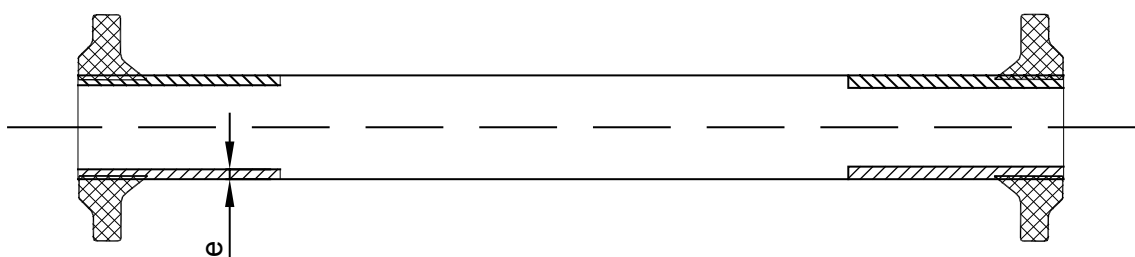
Tubería con bridas incorporadas o con bridas soldadas con casquillo
